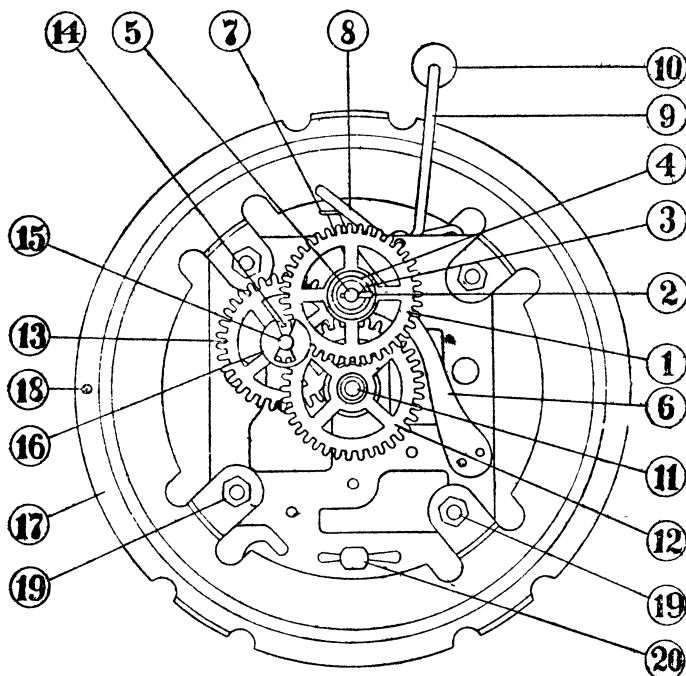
Стрелочные колеса: 1 — сигнальное колесо; 2 — штифт сигнального колеса; 3 — муфта сигнального колеса; 4 — канавка сигнального колеса; 5 — валик сигнального колеса (рис. 2, дет. 20); 6 — защелка; 7 — крючок защелки; служит для пуска и задержки боя; 8 — короткий стержень молоточка; 9 — стержень молоточка (длинный); 10 — молоточек; 11 — ось среднего колеса; 12 — часовое колесо; 13 — подсобное колесо; 14 — трибка подсобного колеса; 15 — брошь; на ней вращается подсобное колесо; 16 — шайба, закрепляющая подсобное колесо на броши 15; 17 — рамка; 18 — отверстия для гвоздиков закрепляющих циферблат; 19 — гайки, прикрепляющие рамку к механизму; 20 — головка переднего центрального винта
